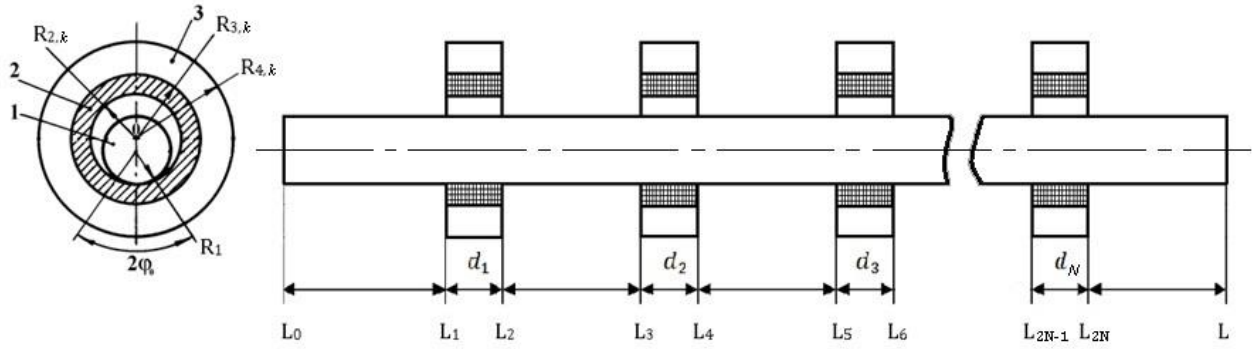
Геометрическая схема систем подшипников скольжения: 1 – вал; 2 – вкладыш (втулка); 3 – обойма (корпус)
